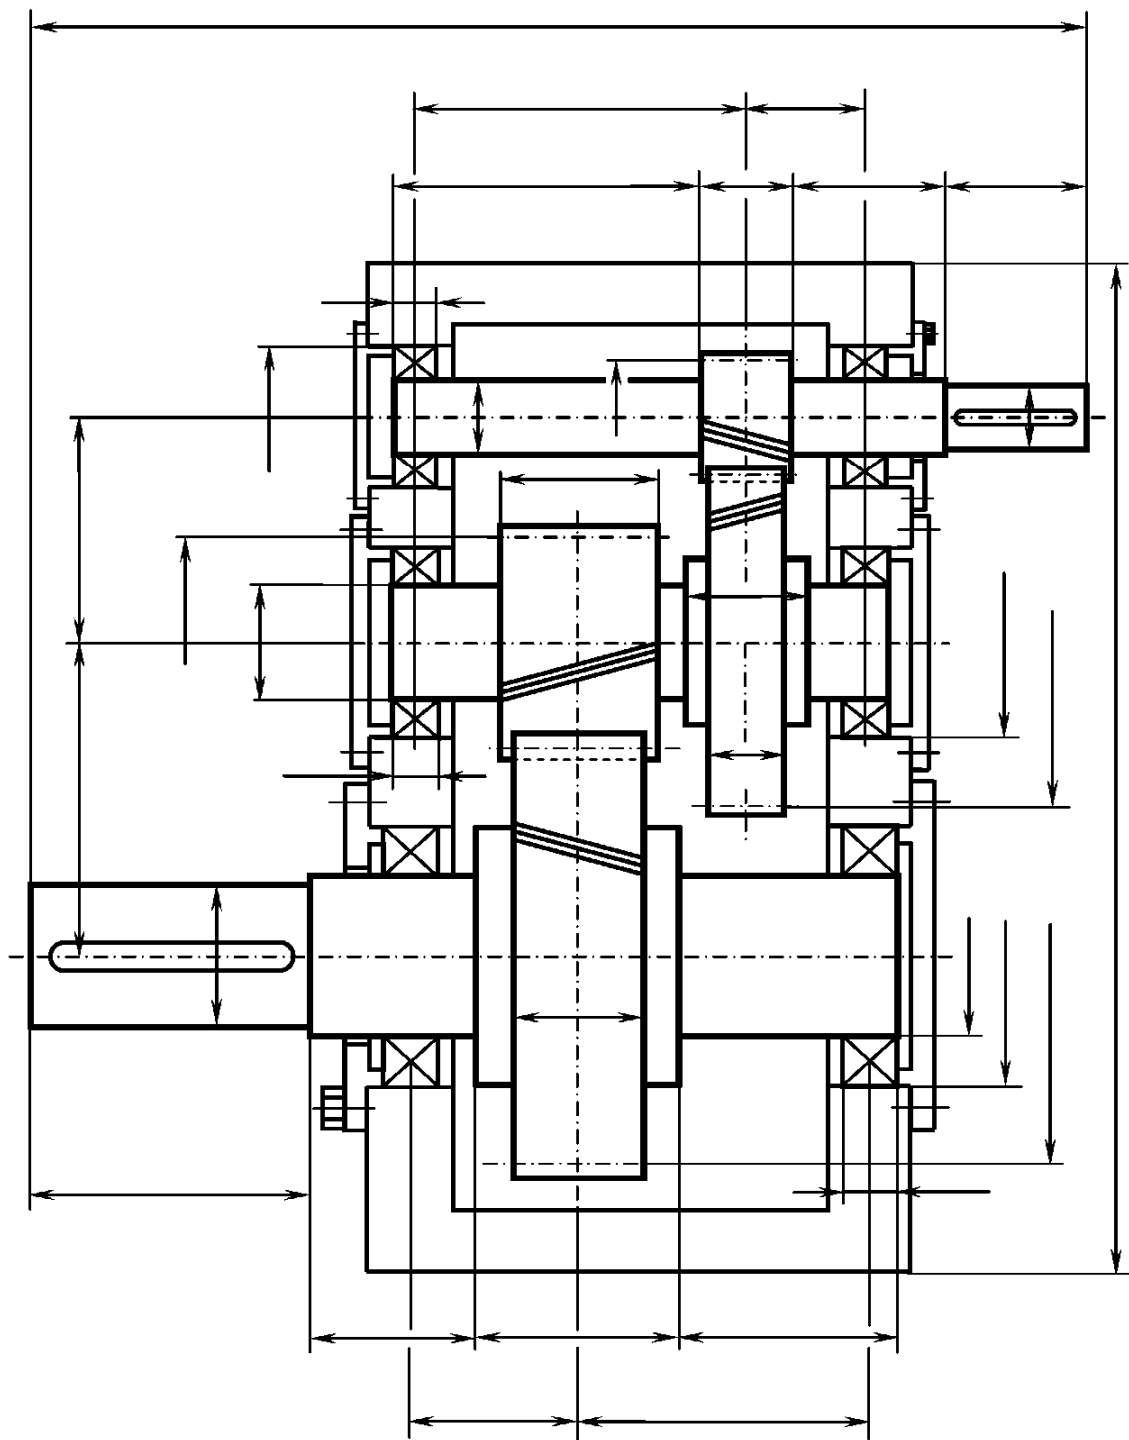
Эскиз компоновки двухступенчатого горизонтального цилиндрического редуктора
